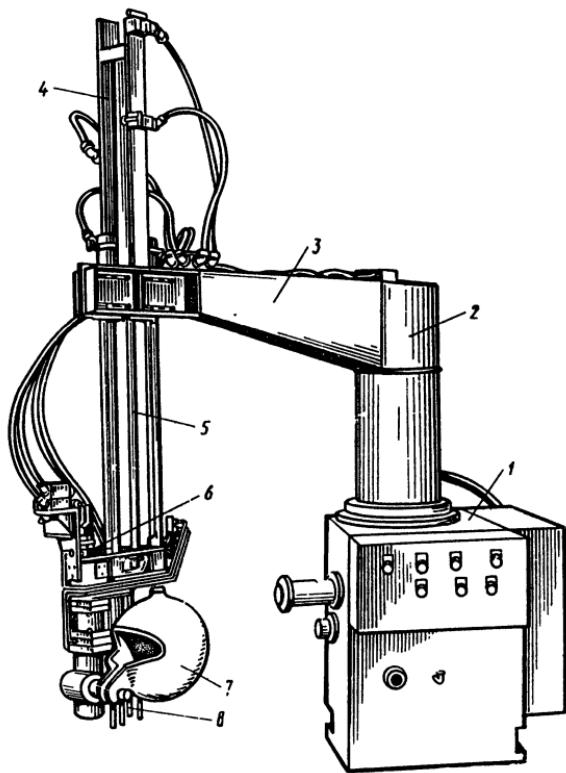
Автоматический ковшовый дозатор расплава:
